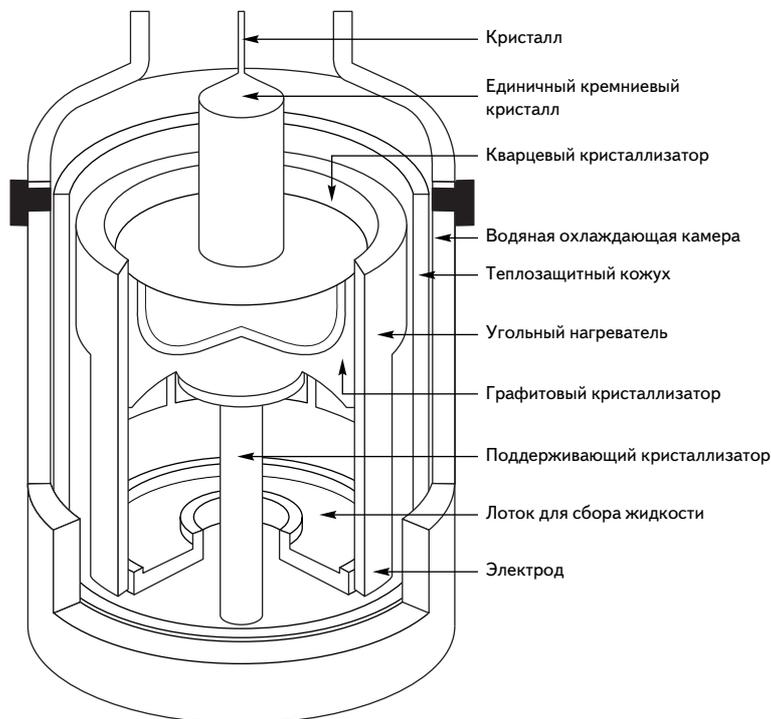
Цилиндрическая кремниевая заготовка создается при большой температуре и высоком давлении
